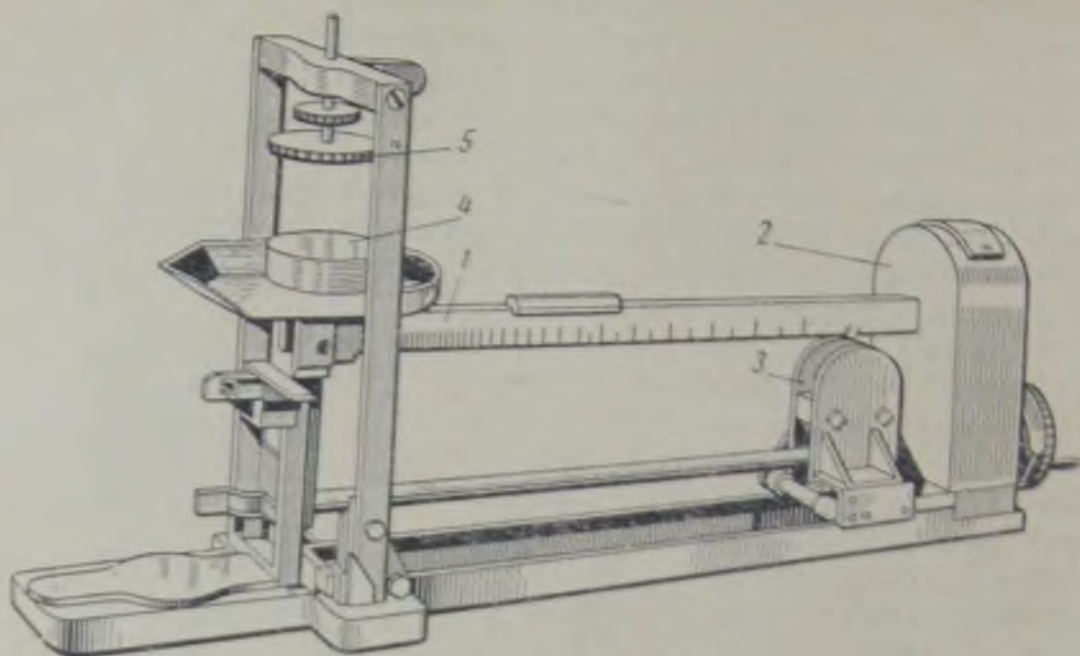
Прибор для определения прочности формовочной смеси на сжатие: 1 — шкала; 2 — груз; 3 — каретка; 4 — подставка для образца; 5 — верхний упор
